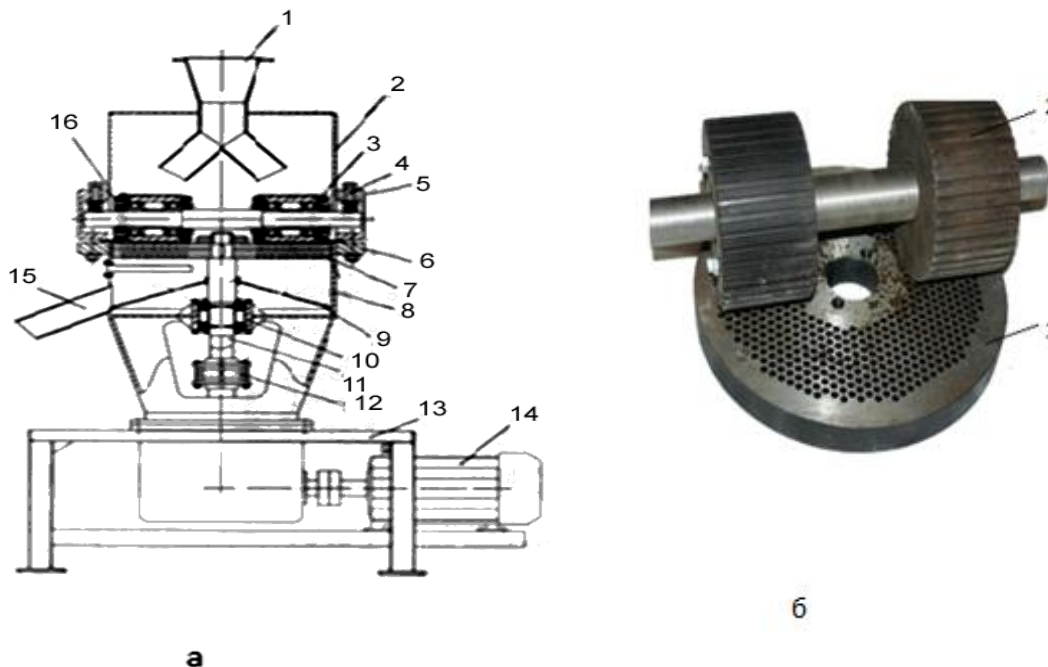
Гранулятор с плоской матрицей: а – общий вид гранулятора; 1– загрузочный бункер; 2 – верхний корпус; 3 – ролик; 4– регулировочный болт; 5 – кожух вала роликов; 6 – фланец; 7 – матрица; 8 – нижний корпус; 9 – коническая вставка; 10 – опора вала; 11 – вал; 12 – муфта; 13 – опора; 14 – привод; б – узел плоской матрицы с прокатывающими роликами: 1 – матрица; 2 – валки
